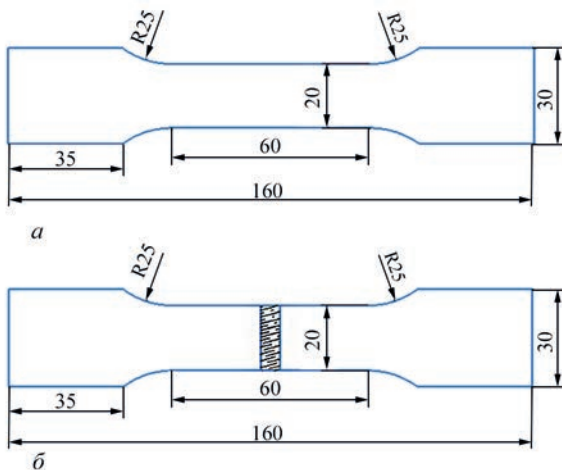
Схеми зразків на розтяг основного металу (а) і металу шва зварного з'єднання (б)
